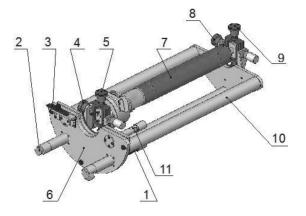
Излучающий модуль на основе газового лазера: 1 — рукоятка затяжки основания; 2 — прижим; 3 — щуп; 4, 5 — ручки переднего регулировочного узла для перемещения излучателя по горизонтали и вертикали соответственно; 6 — основание излучателя; 7 — излучатель; 8, 9 — ручки заднего регулировочного узла для перемещения лазерного пучка по горизонтали и вертикали соответственно; 10 — кронитейн; 11 — рукоятка зажима кронитейна
